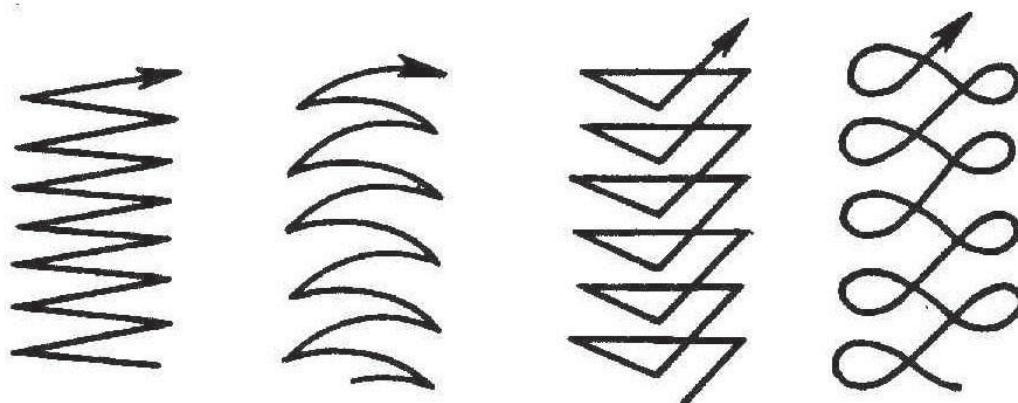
Колебательные движения электрода при ручной дуговой сварке
